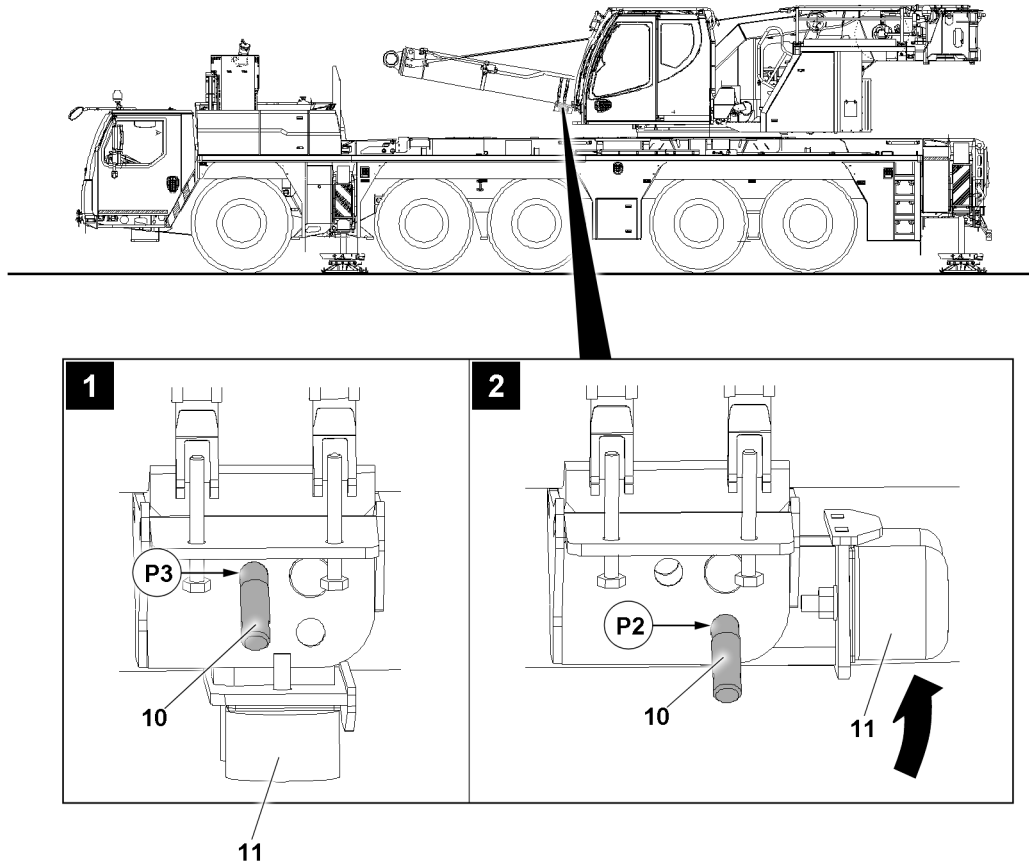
Rebater a patola do cilindro de basculamento para baixo
